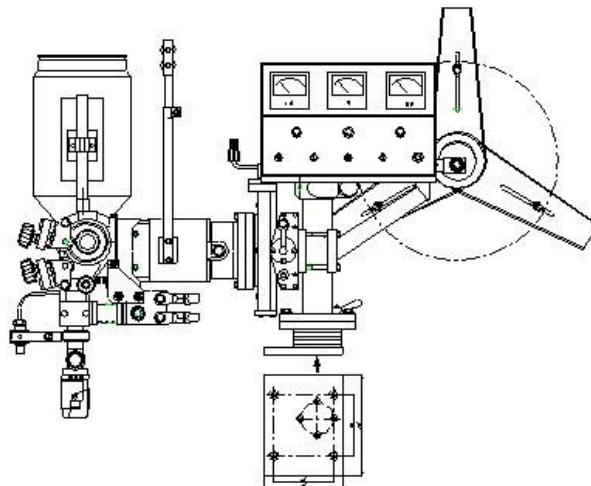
Сварочная головка АДФ - 1250[14]
